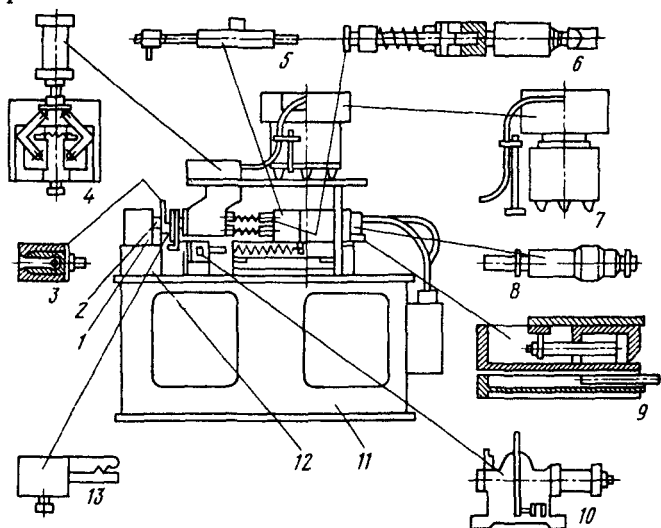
Компоновка полуавтомата для завертывания шпилек из агрегатных модулей:
